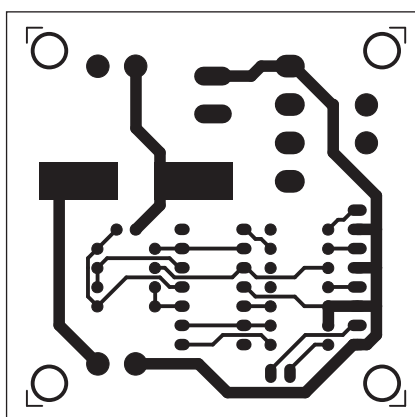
Obrazec desky spojů nabíječky (strana TOP)
